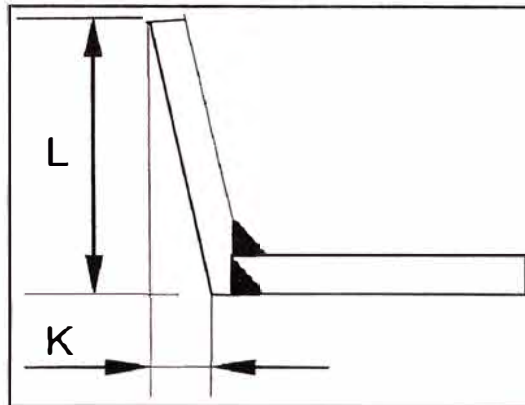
Secciones soldadas, tolerancia. Se requiere penetración de soldadura total.
